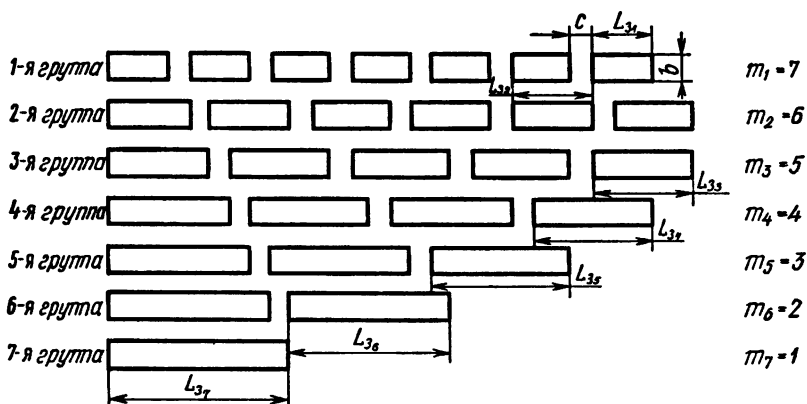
Заготовки, подвергаемые торцовому фрезерованию фрезами с режущими пластинами из композита
